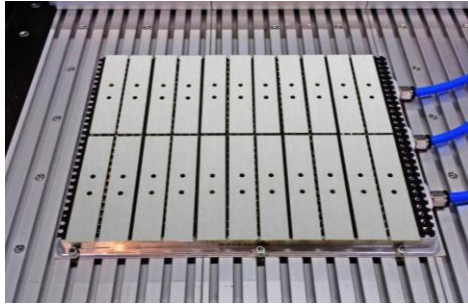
Изготовление элемента конструктивно-подобного образца на перфорированном вакуумном столе
